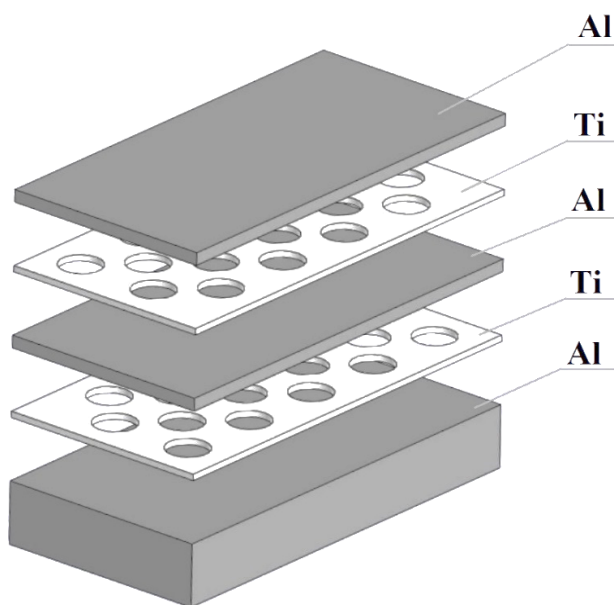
Схема сборки пакета композиционного материала перед сваркой взрывом
